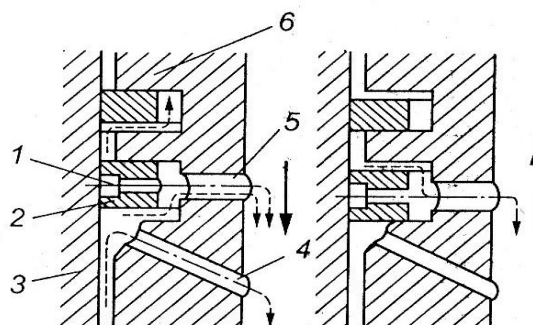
Схема работы маслосъемных поршневых колец (сплошными линиями показано направление движения поршня, штриховыми – масла): 1 – прорезь в кольце; 2 – маслосъемное кольцо; 3 – цилиндр; 4 – отверстие в поршне; 5 – отверстие в канавке кольца; 6 – поршень
